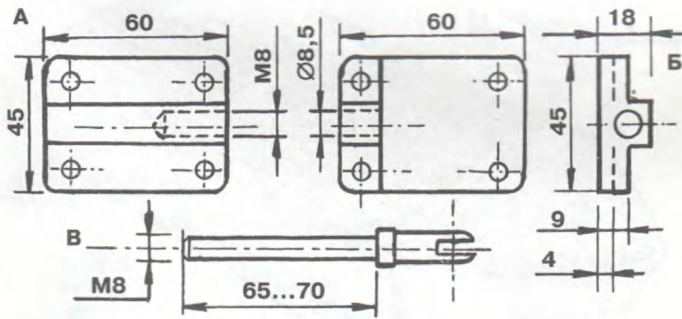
Детали разъема: А — первый (по ходу движения), Б — второй, В — винт.
